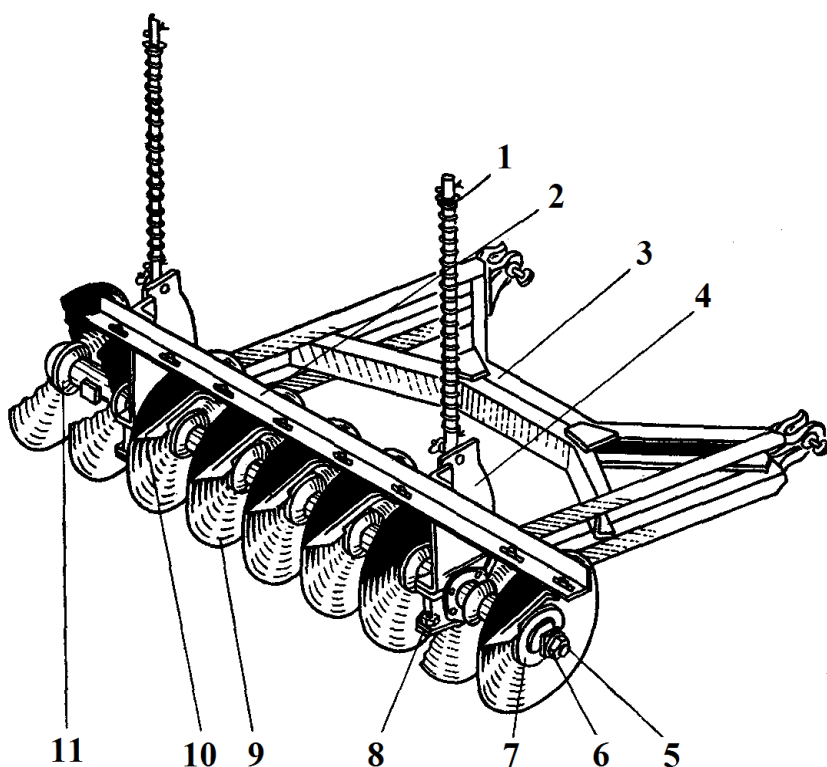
Права секція: 1 - штанга з пружиною; 2 - кутник скребків; 3 - рамка; 4 - кронштейн; 5 - вісь батареї; 6 - гайка; 7 - шайба; 8 - підшипник; 9 - диск; 10 - скребок; 11 - шпуля
